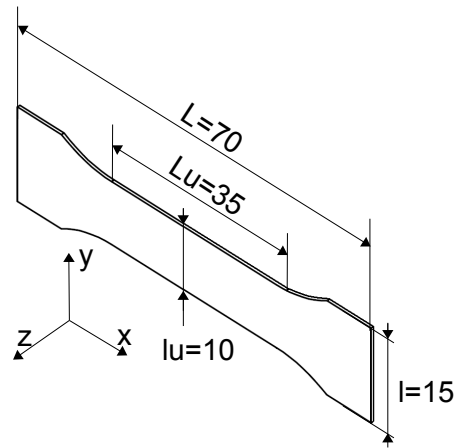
Géométrie et dimensions de l'éprouvette de traction uniaxiale (cotes en mm).
